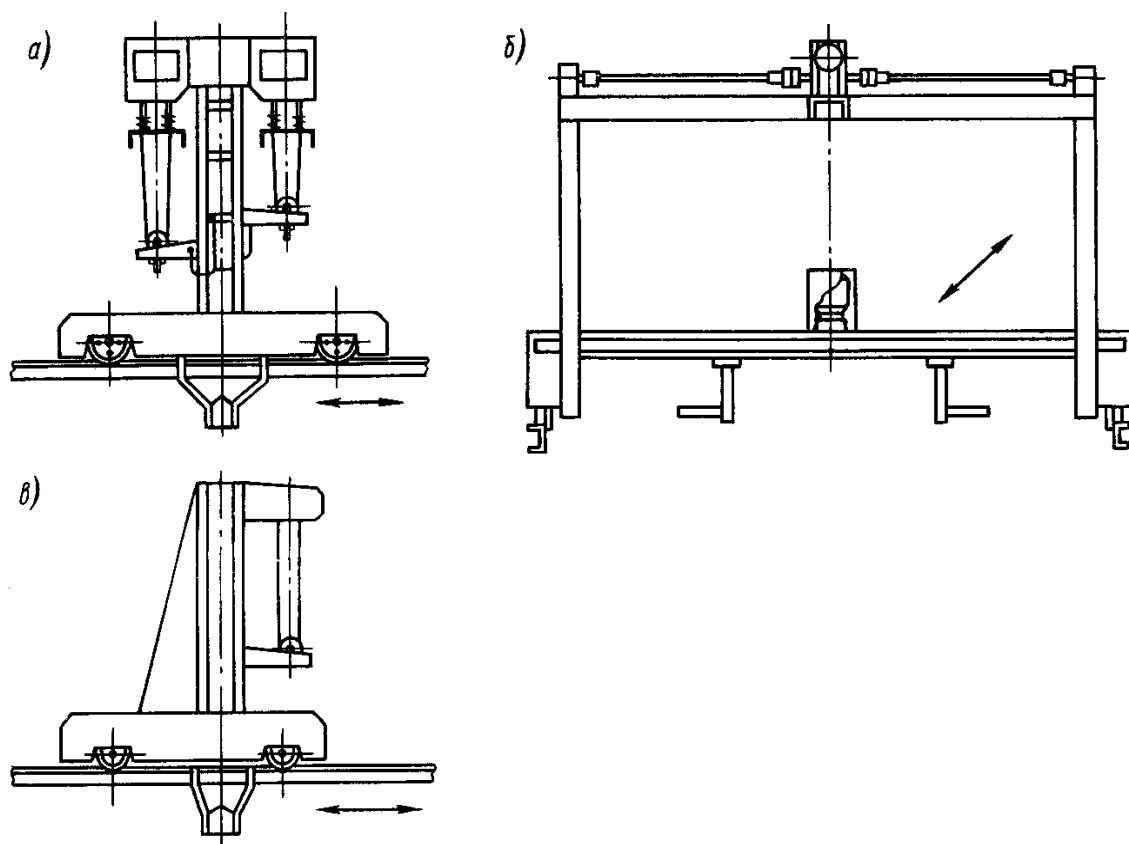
Автооператоры порталные: а – двухзахватный вид (вид сбоку); б – однозахватный с консолью (вид сбоку); в – однозахватный с грузозахватом по оси подъема (главный вид).
